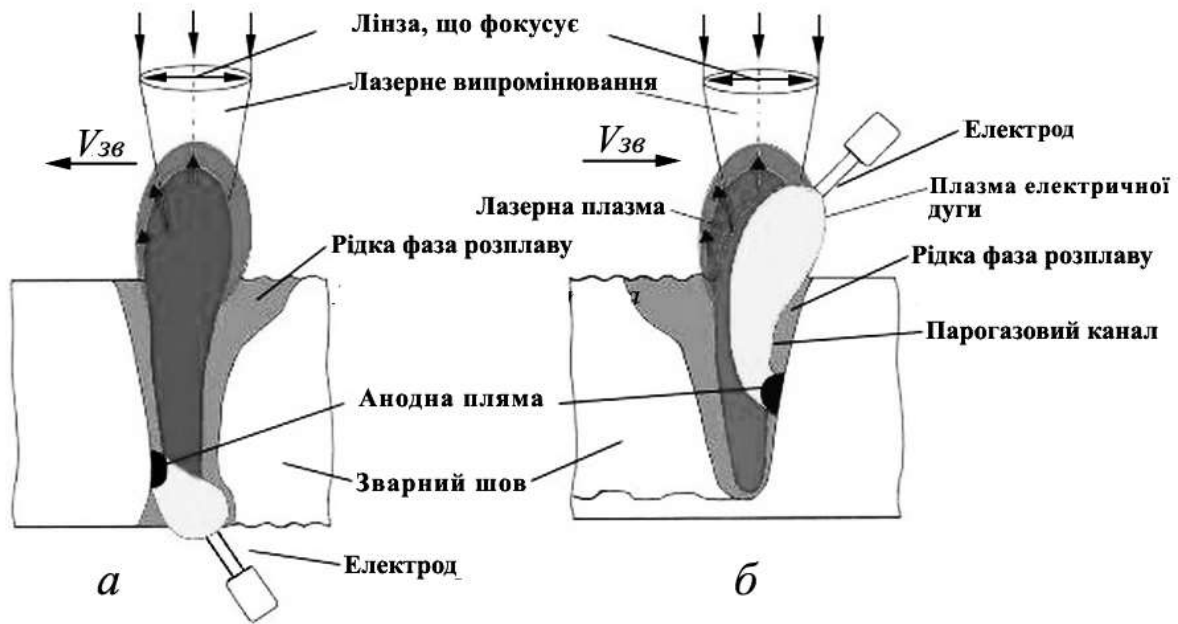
22. Геометричні схеми реалізації процесу лазерно-дугового зварювання
